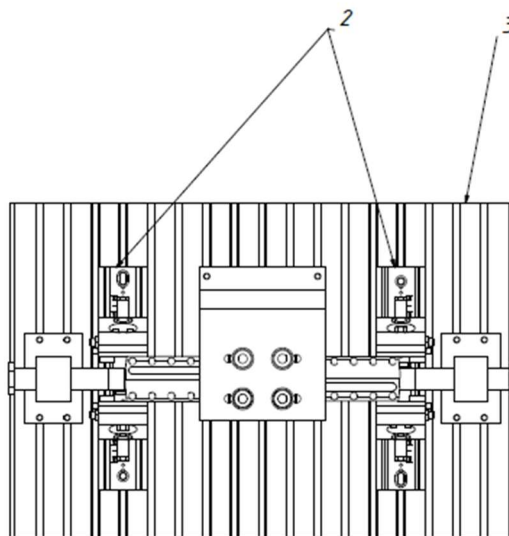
Свердильний пристрій (Вид 2)
